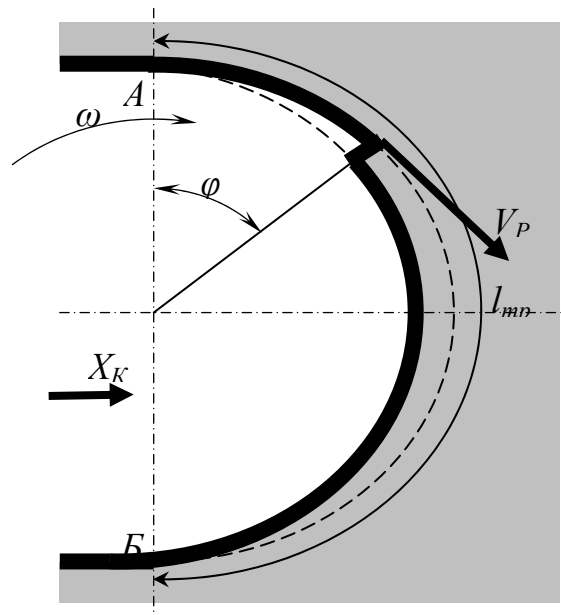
Путь трения каждой отдельной точки режущей кромки серийного режущего инструмента
